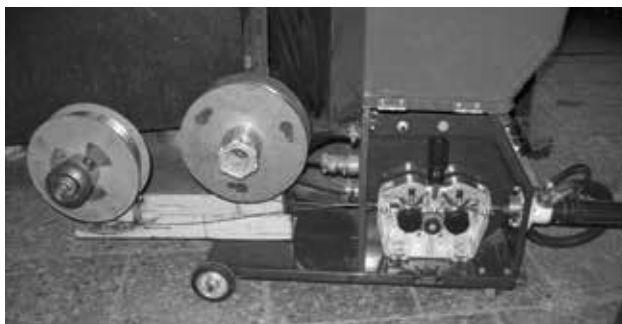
Двухэлектродный сварочный аппарат
